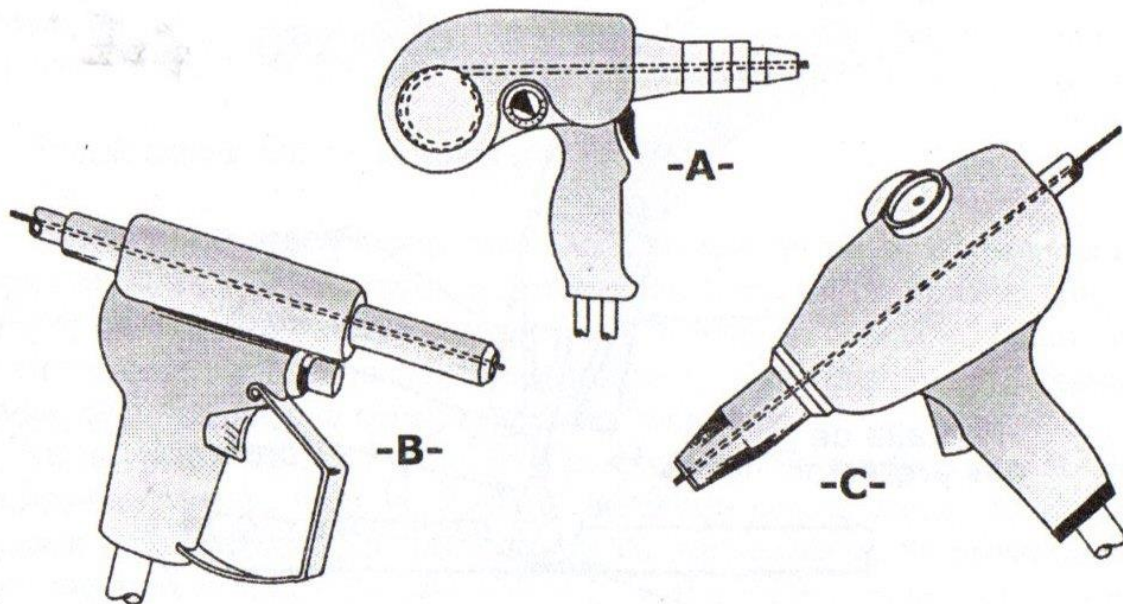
Ilustraciones de los tipos de pistolas para soldadura MIG
